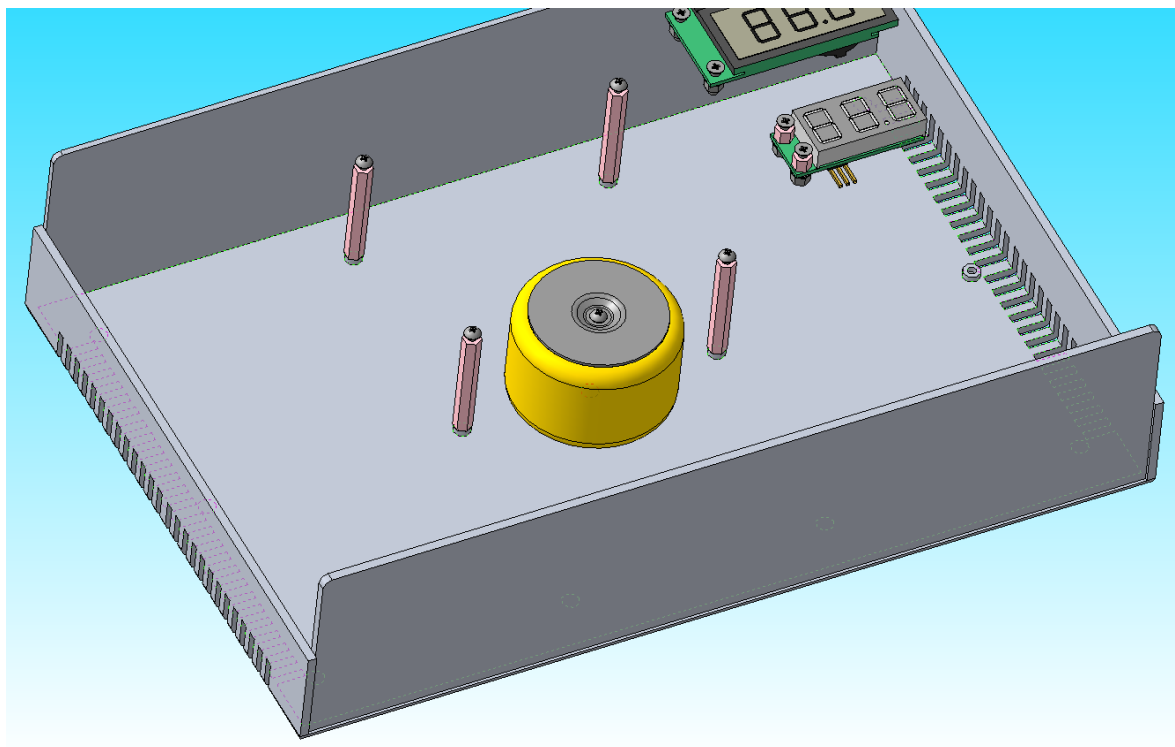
Расположение в корпусе трансформатора (крышка корпуса не показана).
